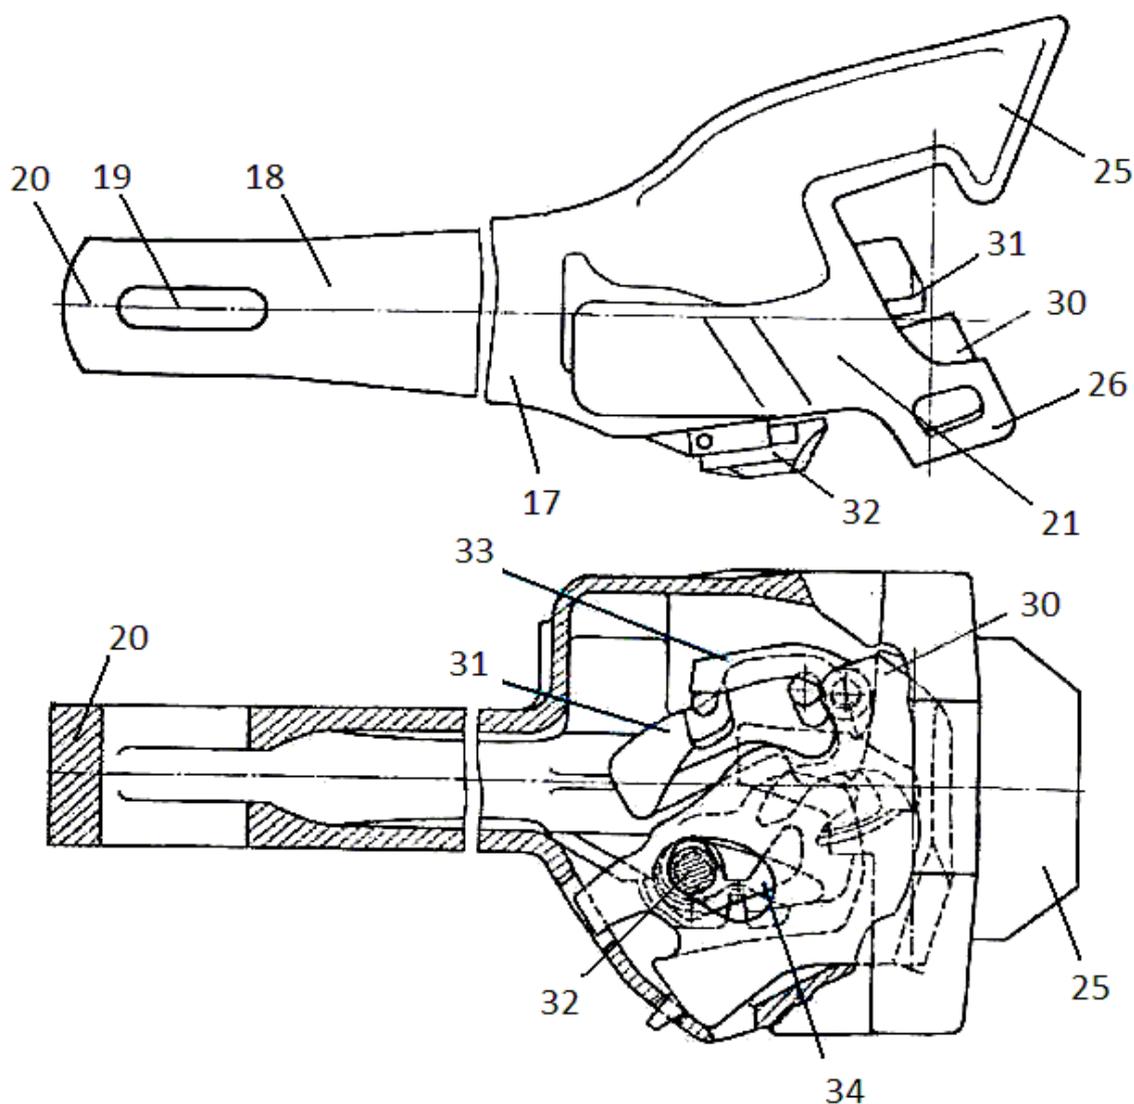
Автосцепка, корпус (поз 17), механизм сцепления (поз.29)
